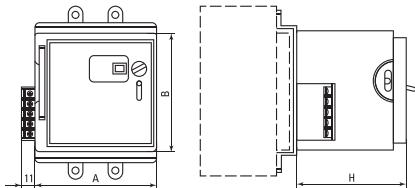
Габаритные размеры приводов 250, 400, 800, 1600, CD/2
